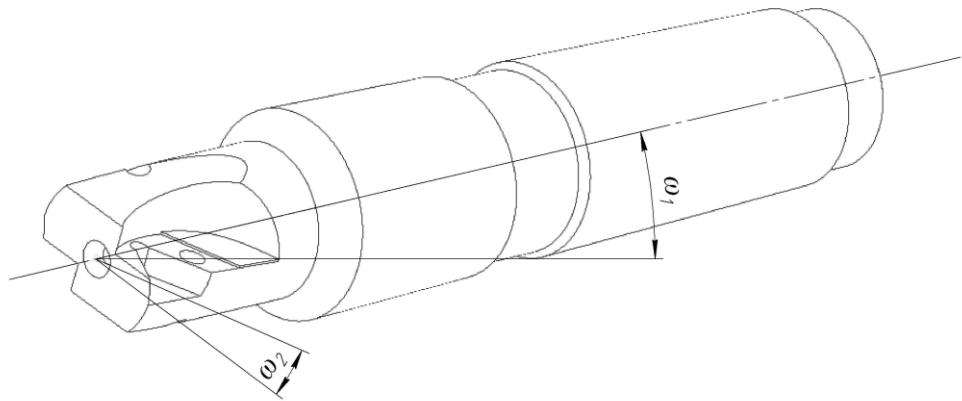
Фрезерування опорної поверхні під пластину на корпусі фрези
